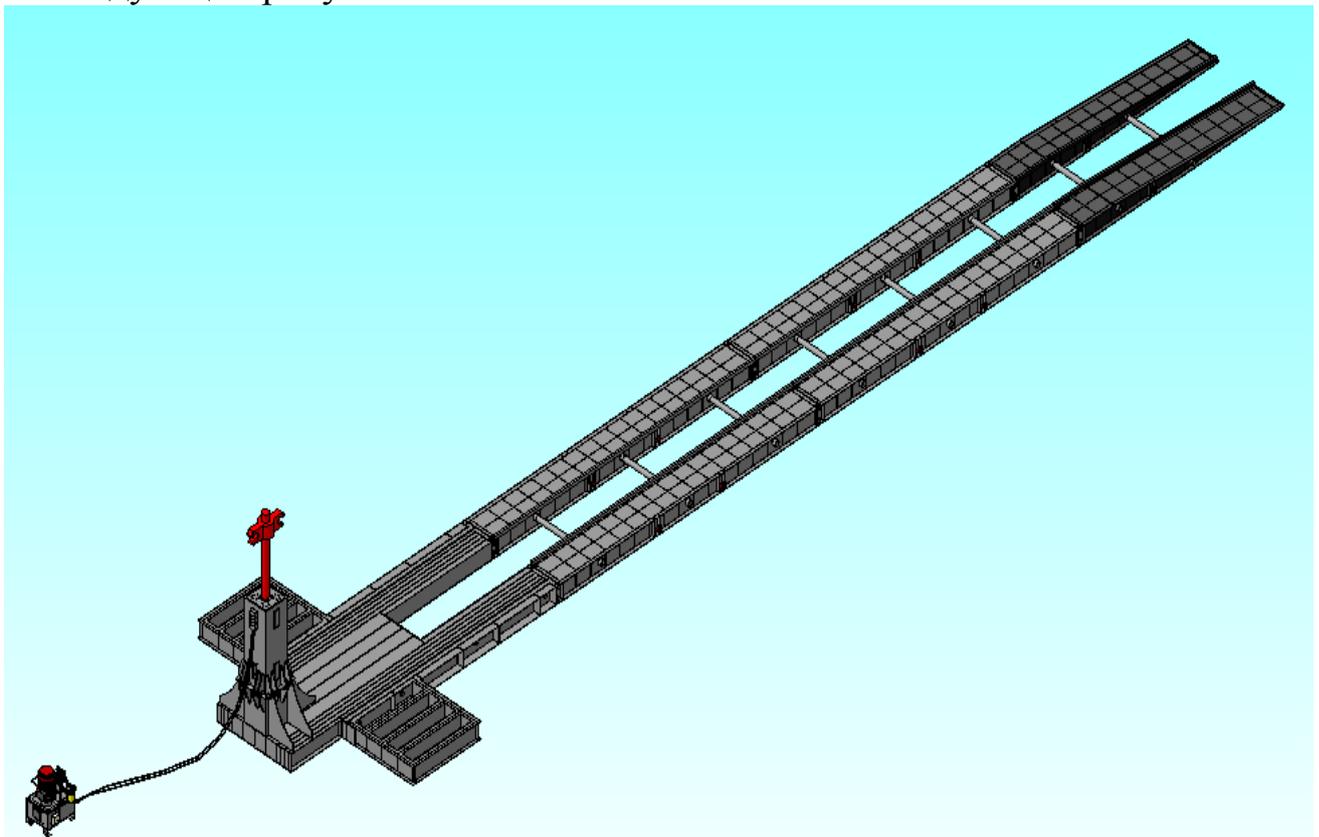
Устройство для проверки на прочность мачтовой конструкции агрегата для бурения и ремонта скважин APC – 250
